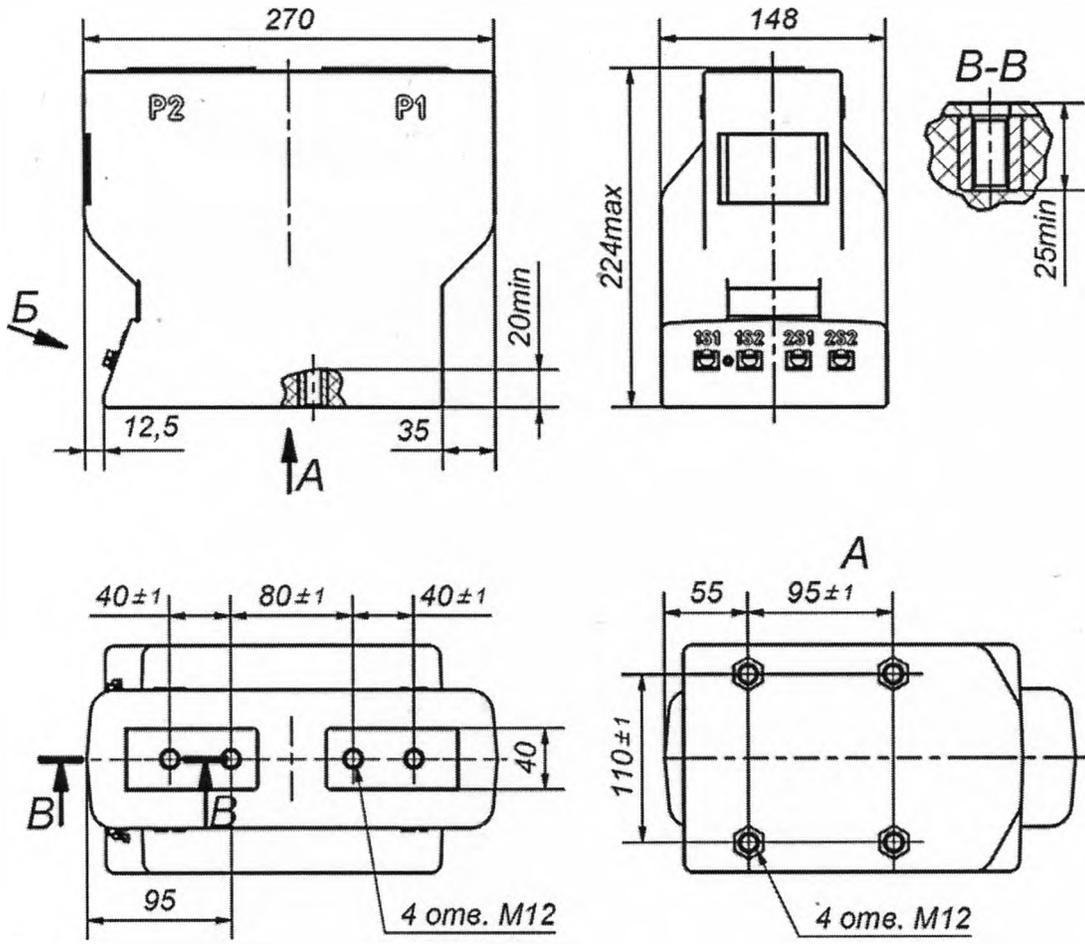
Габаритный чертёж трансформатора тока ТОЛУ-10-2.2-Г2.
